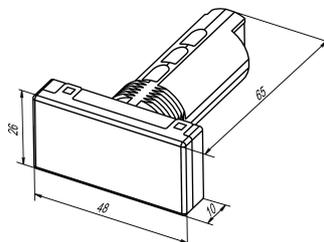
Габаритные размеры корпуса Щ9
